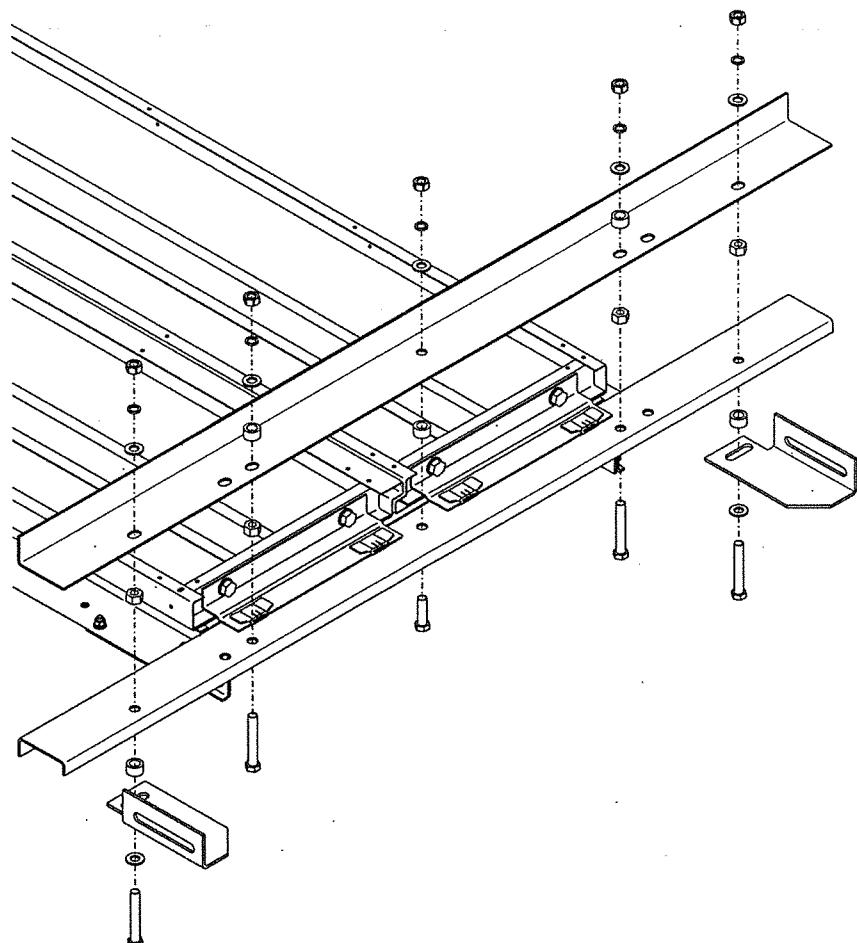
Сборка порога двери шахты с помощью болтов
